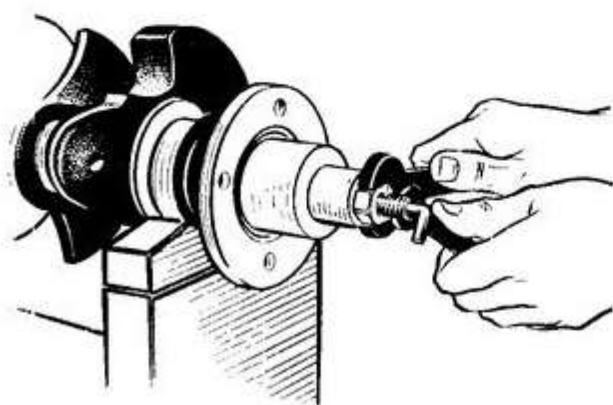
Выпрессовка подшипника первичного вала коробки передач из коленчатого вала
